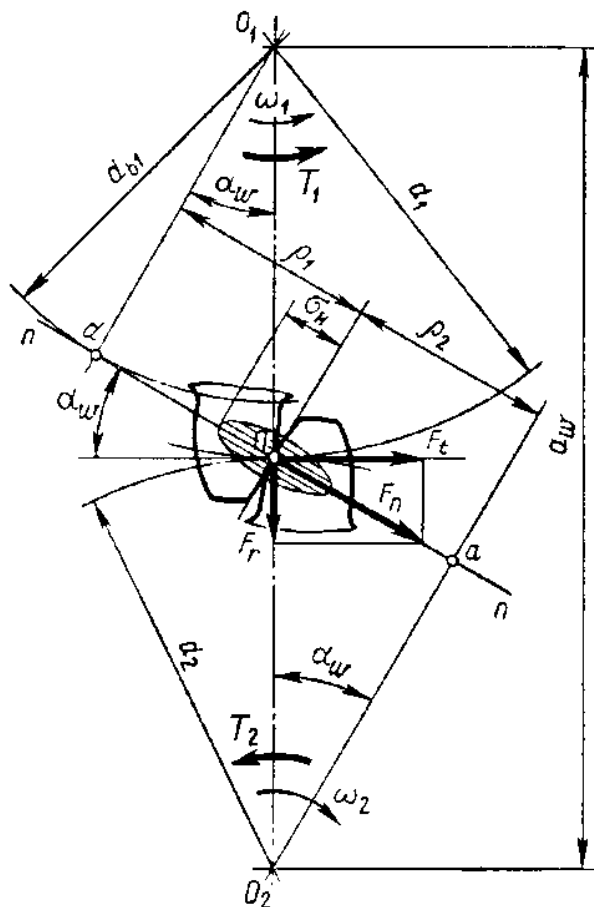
Силы в зацеплении прямозубой цилиндрической передаче
